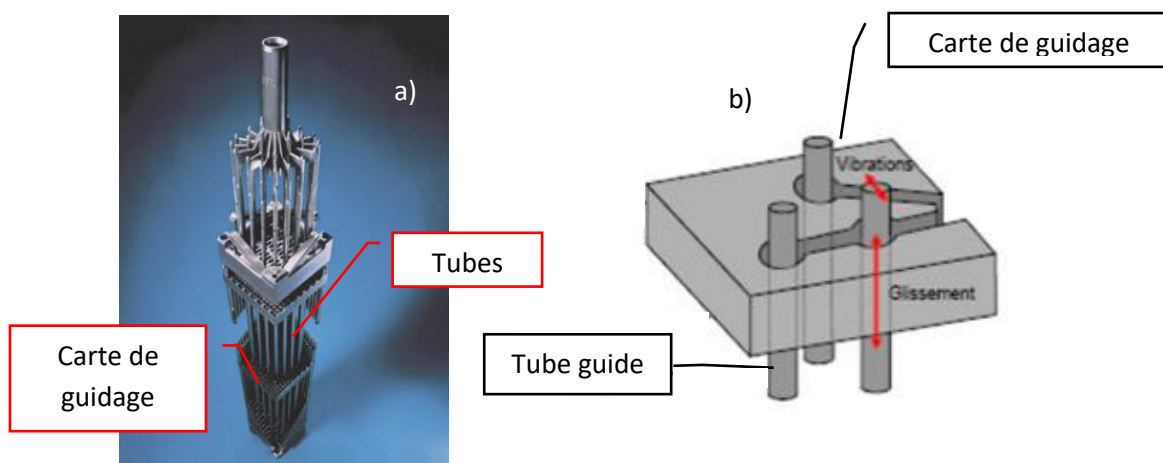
Position des tubes guides dans un assemblage combustible pour REP : a) assemblage complet ; b) détails carte de guidage
